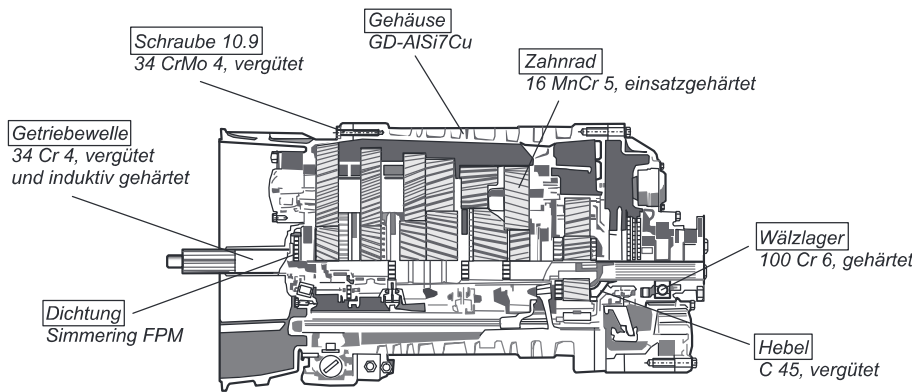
Verwendung verschiedenen Werkstoffe in einem Nutzfahrzeuggetriebe [2.3]
